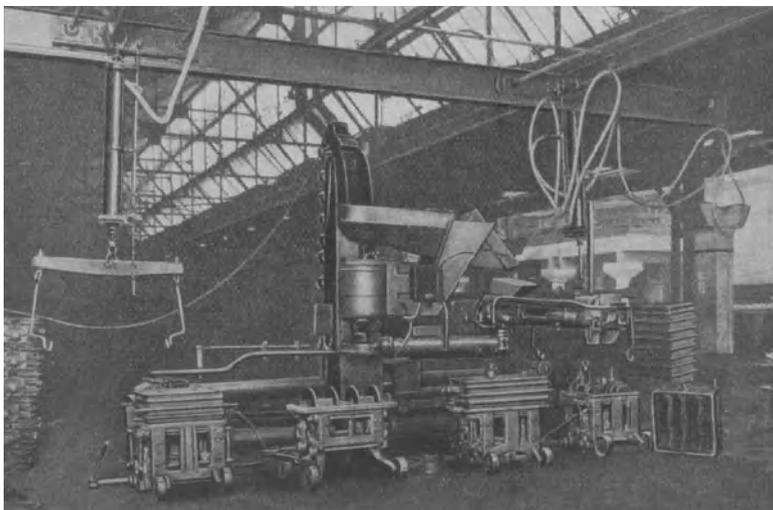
Trecker-Sandschleuderer mit angesellten Abhebemaschinen.
